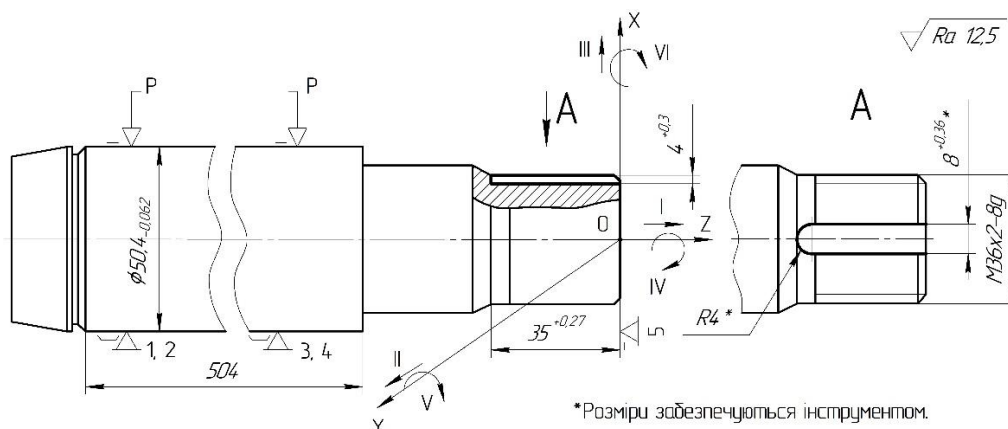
Ескіз заготовки на операції 030. Схема № 1
